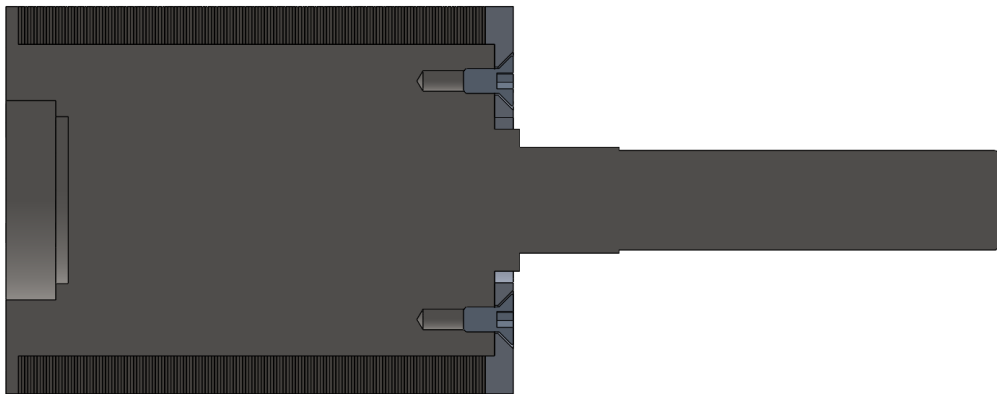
Guidage et compression des tôles du rotor haute vitesse (vue en coupe)
